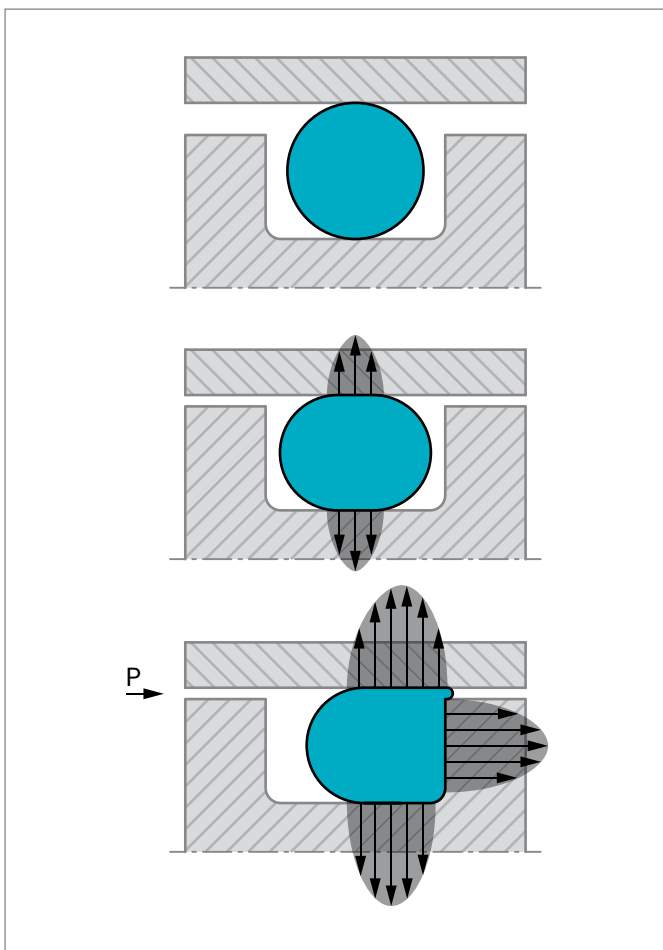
O-Ring-Anpresskräfte mit und ohne Systemdruck
